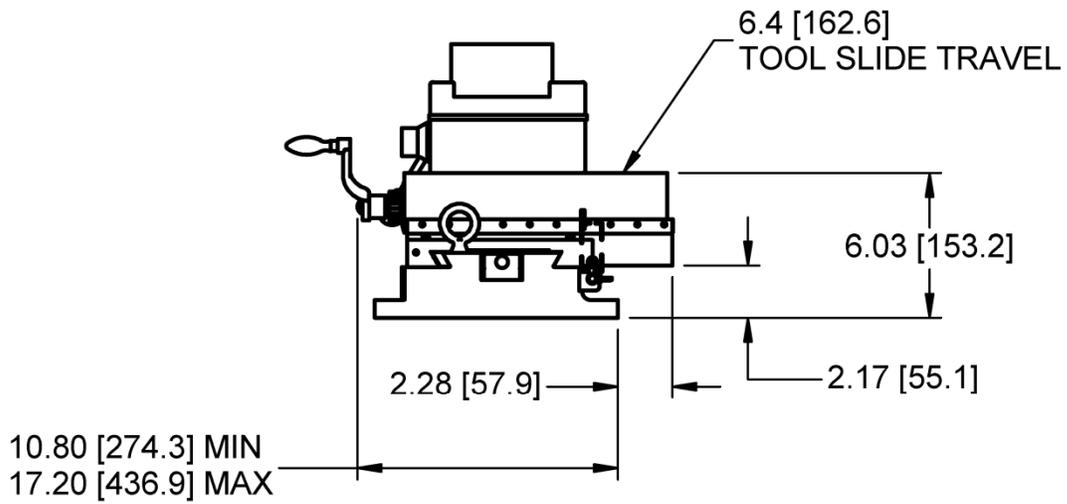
DIMENSIONS DU BLOC OUTIL (POUCES ET MILLIMETRES)
